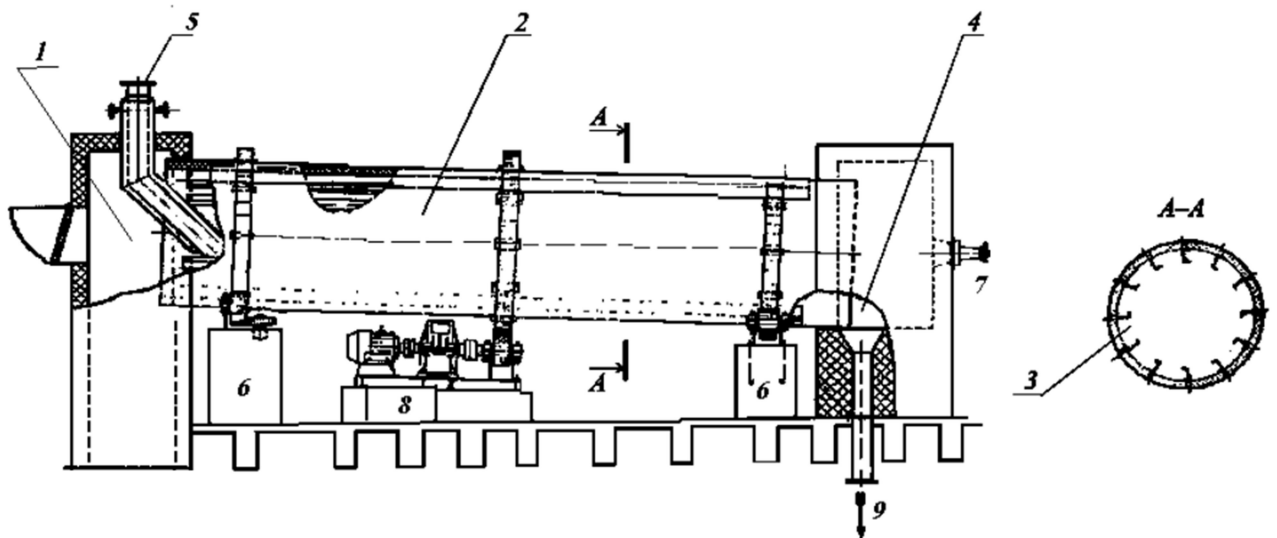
Общий вид вращающейся барабанной сушилки: 1 – камера нагрева, 2 – вращающийся барабан, 3 – полки насадки, 4 – выгрузочная камера, 5 – загрузочная течка, 6 – опорные станции, 7 – смотровой лючок, 8 – приводная станция, 9 – выгрузочная течка
